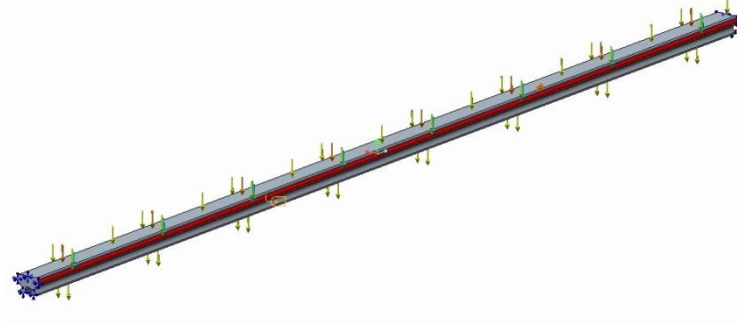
Άσκηση κάθετης δύναμης 10kg στο μέσο του οδηγού κύλισης.
